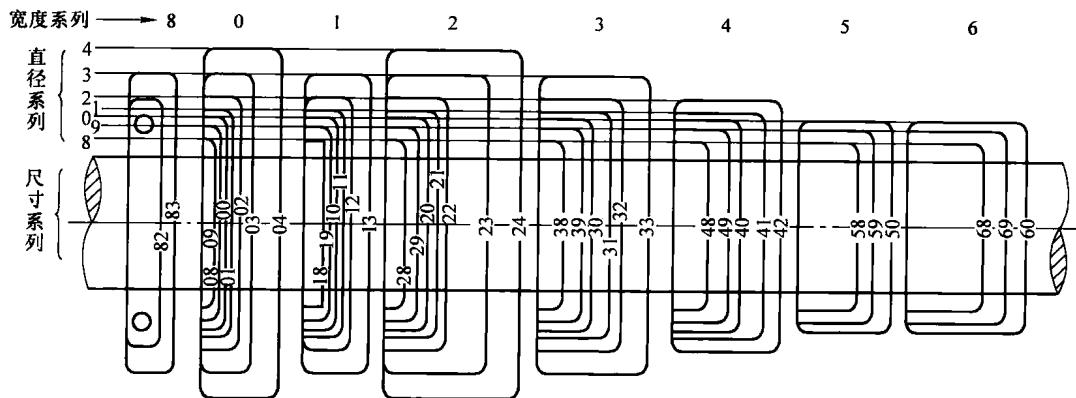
向心轴承的尺寸系列示意图（圆锥滚子轴承除外）
